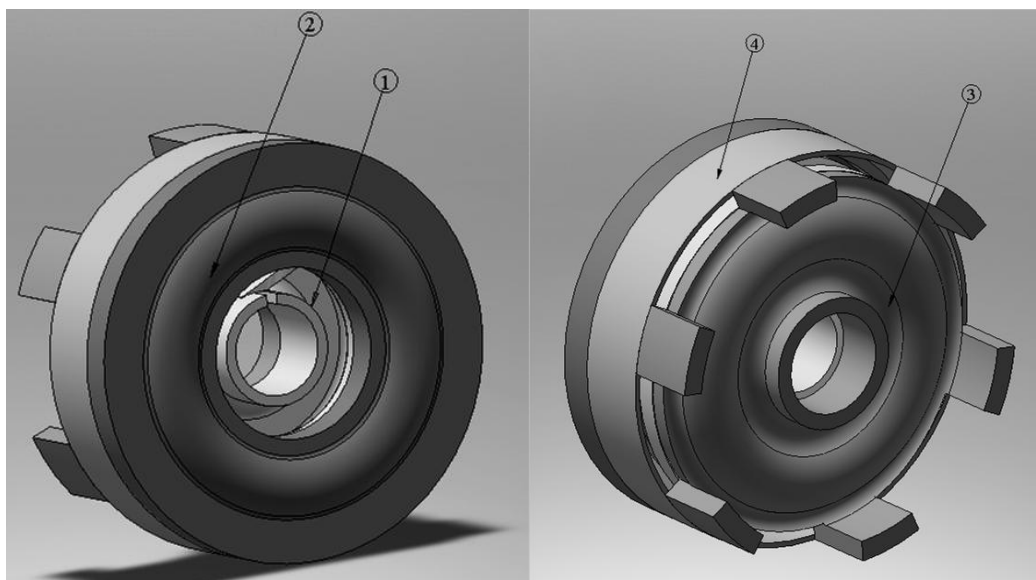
Загальний вид ступені: 1 – робоче колесо; 2 – передня вихрова ступінь; 3 – задня вихрова ступінь; 4 – корпус робочого колеса
